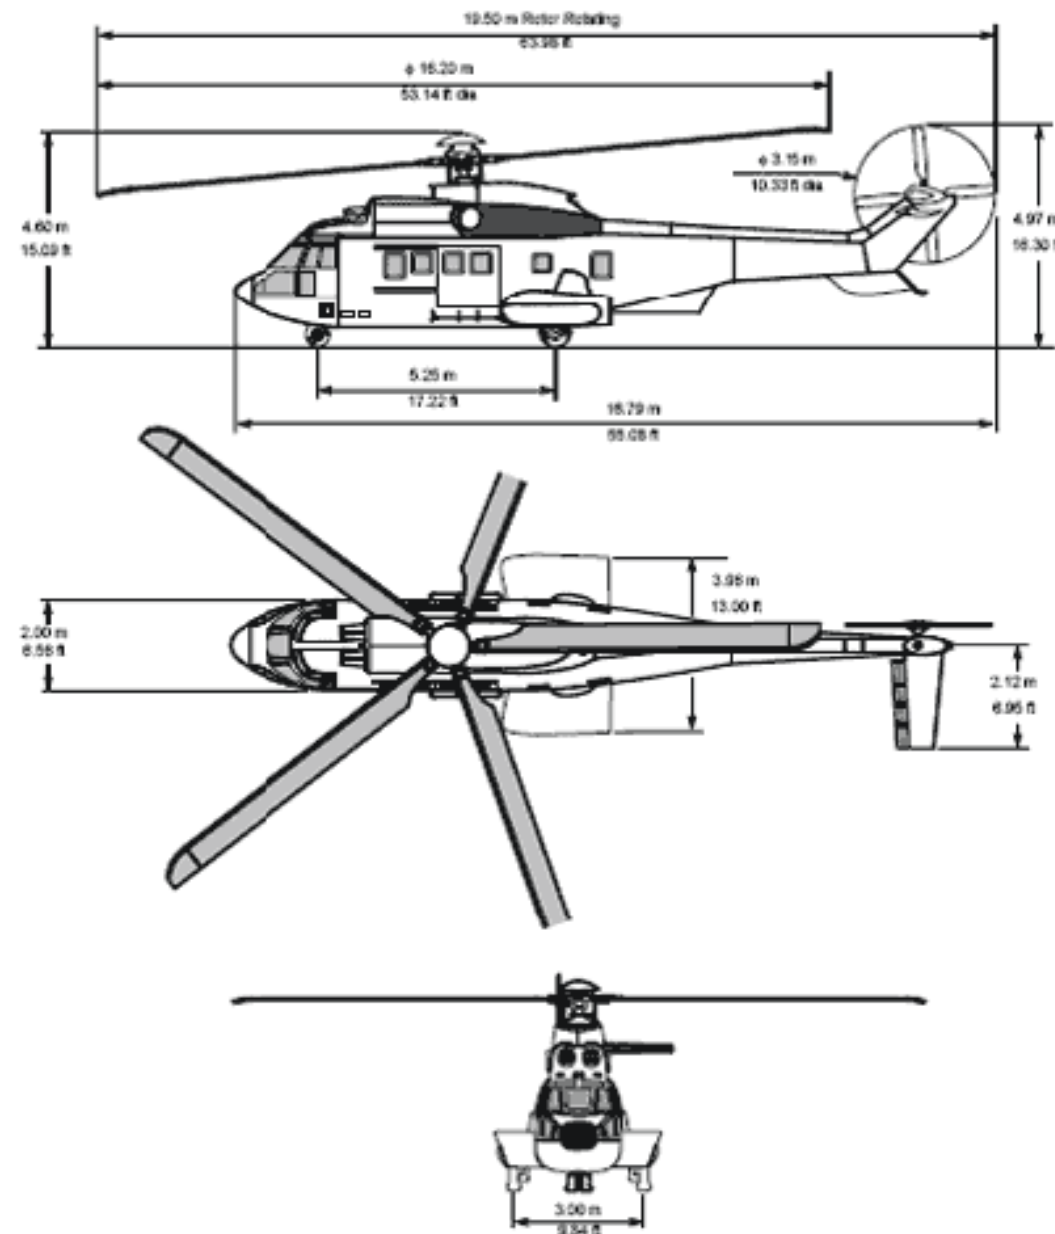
Dimensiones del EC225. Fuente: Airbus.
